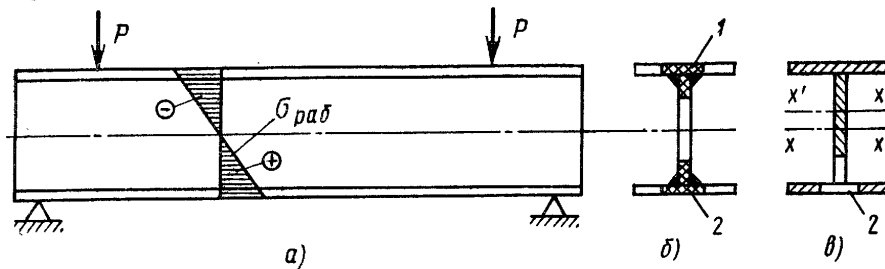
Схемы нагружения сварной балки с остаточными напряжениями:
